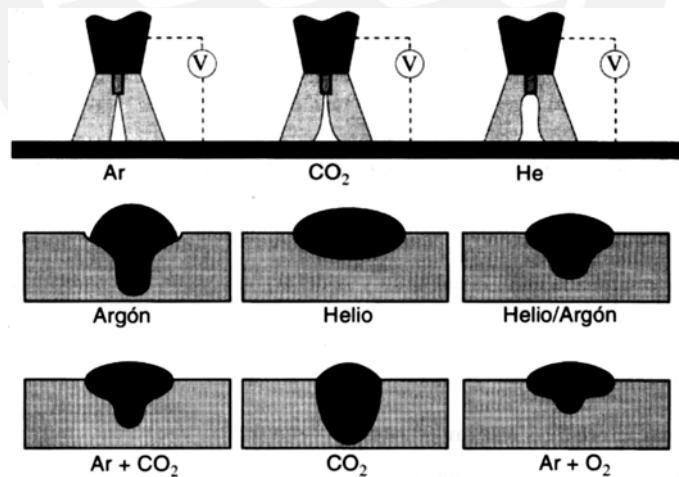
Soldadura GMAW con diferente gas protector [1]
